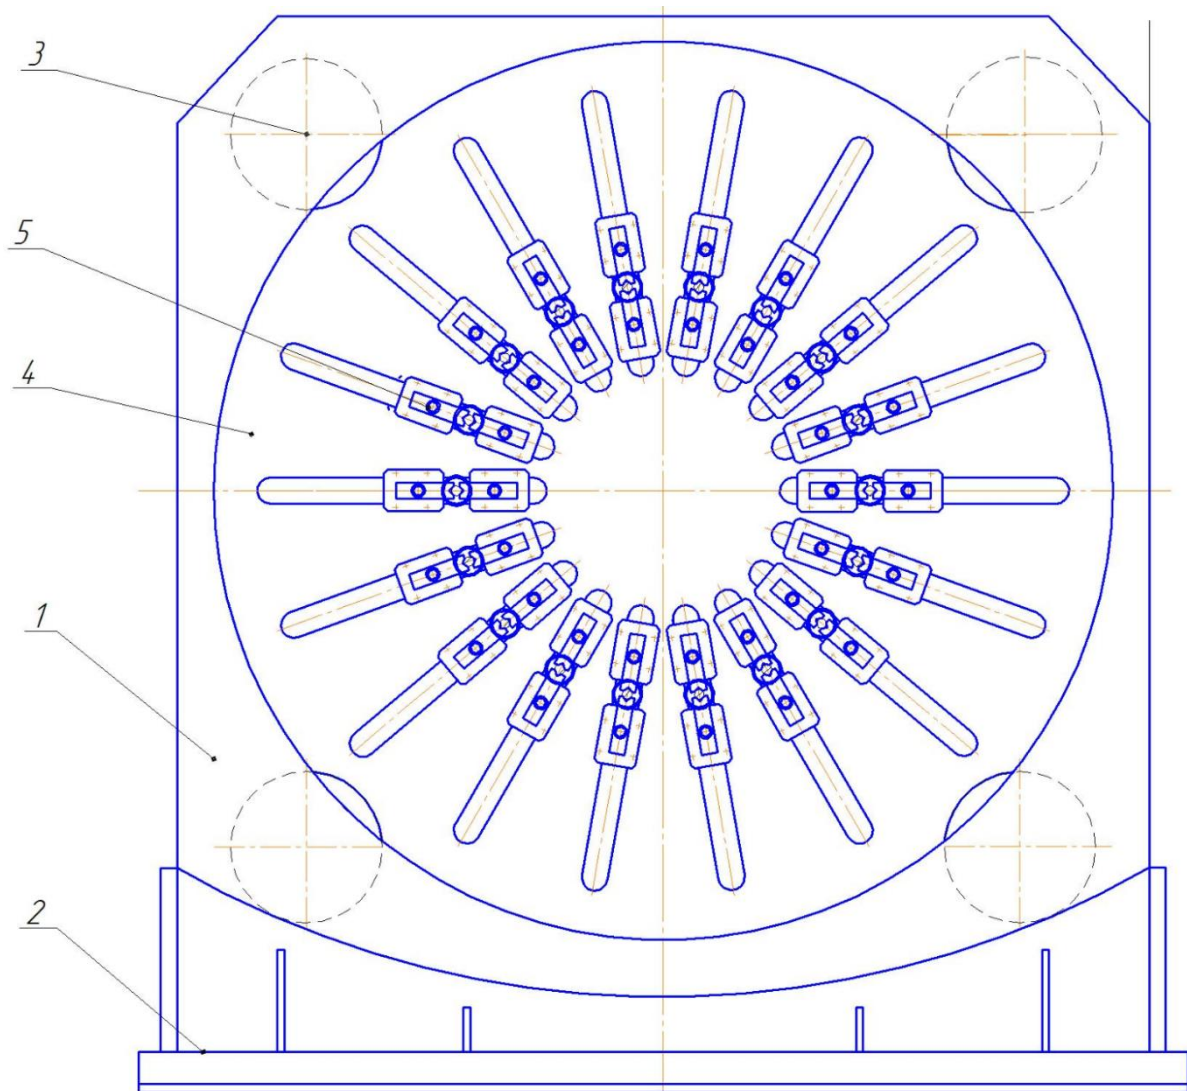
Схематичне зображення нерухомої головки: 1 – несуча рама; 2 – основа верстату; 3 – напрямлюючі ролики; 4 – ведучий диск; 5 – гідравлічні затискачі
